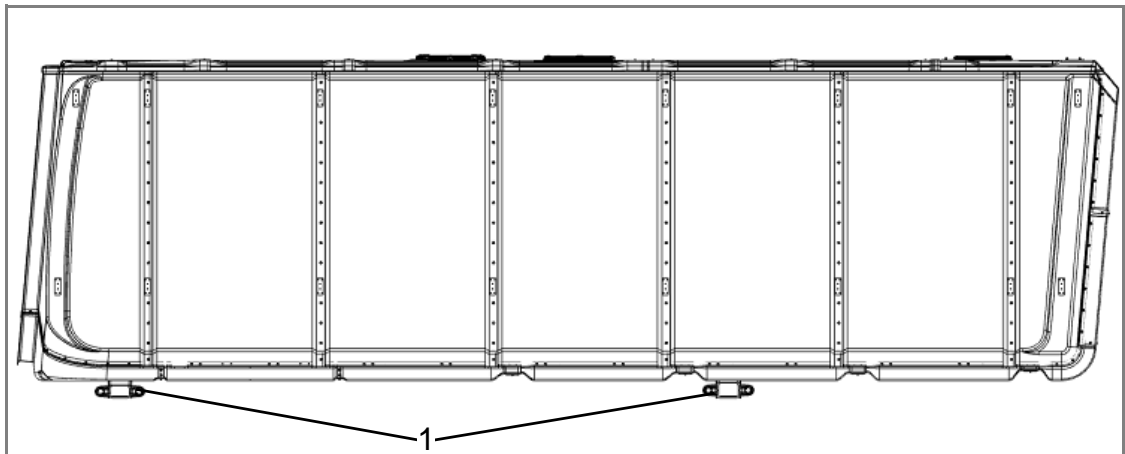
Beispieldarstellung Maschinenhaus, Ansicht seitlich mit Transportfüßen (1)
